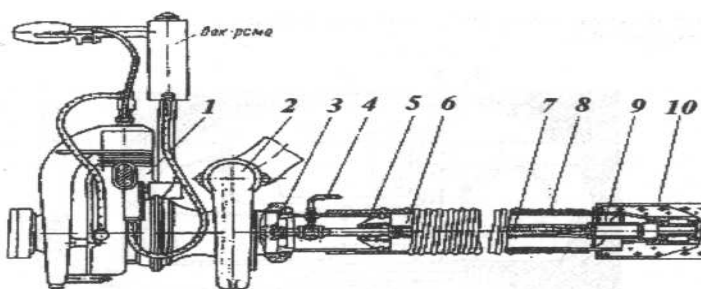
Малогабаритная мотопомпа МЛН-2,5/0,25: 1 - двигатель; 2 - центробежный насос; 3 — полумуфта; 4 - ручка-переключатель; 5 - направляющая втулка; 6 - хвостовик; 7 - гибкий вал; 8 — всасывающий рукав; 9 - осевой насос; 10 — сетчатый фильтр
